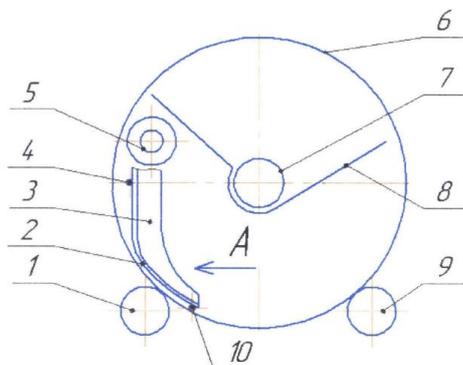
Циліндричний трієр за конструкцією Кузнецова В.В.; 1 – опорні ролики; 2 – живильний лоток; 3 – реборда; 4, 10 – гвинтові механізми; 5 – подаючий шнек; 6 – циліндр; 7 – вивідний шнек; 8 – поворотний лоток; 9 – приводні ролики.
